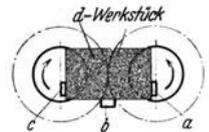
Schraubenfedern zum Füllen von Stapelvorrichtungen. a rechter Führungsstege, c linker „, b unterer „, d Werkstück, e Vorschubfedern.
